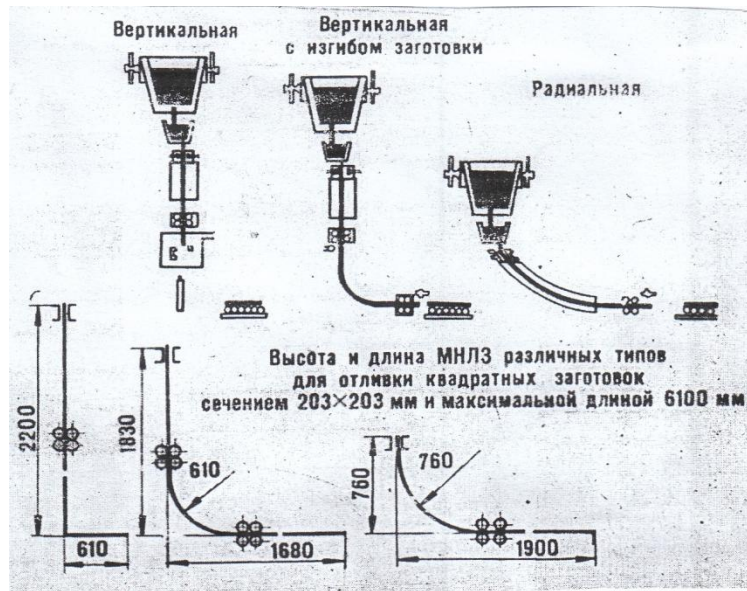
Типы машин непрерывного литья заготовок
